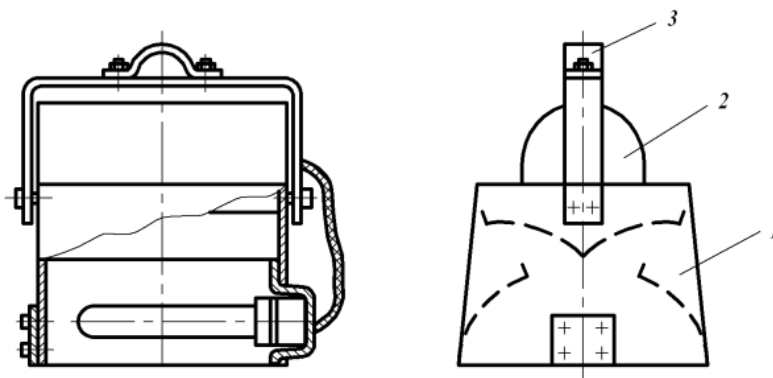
Елементи конструкції опромінювача ЖСП18-400-001-ХЛ4: 1 – корпус з дзеркальним відбивачем; 2 – блок ПРА; 3 – вузол підвісу
